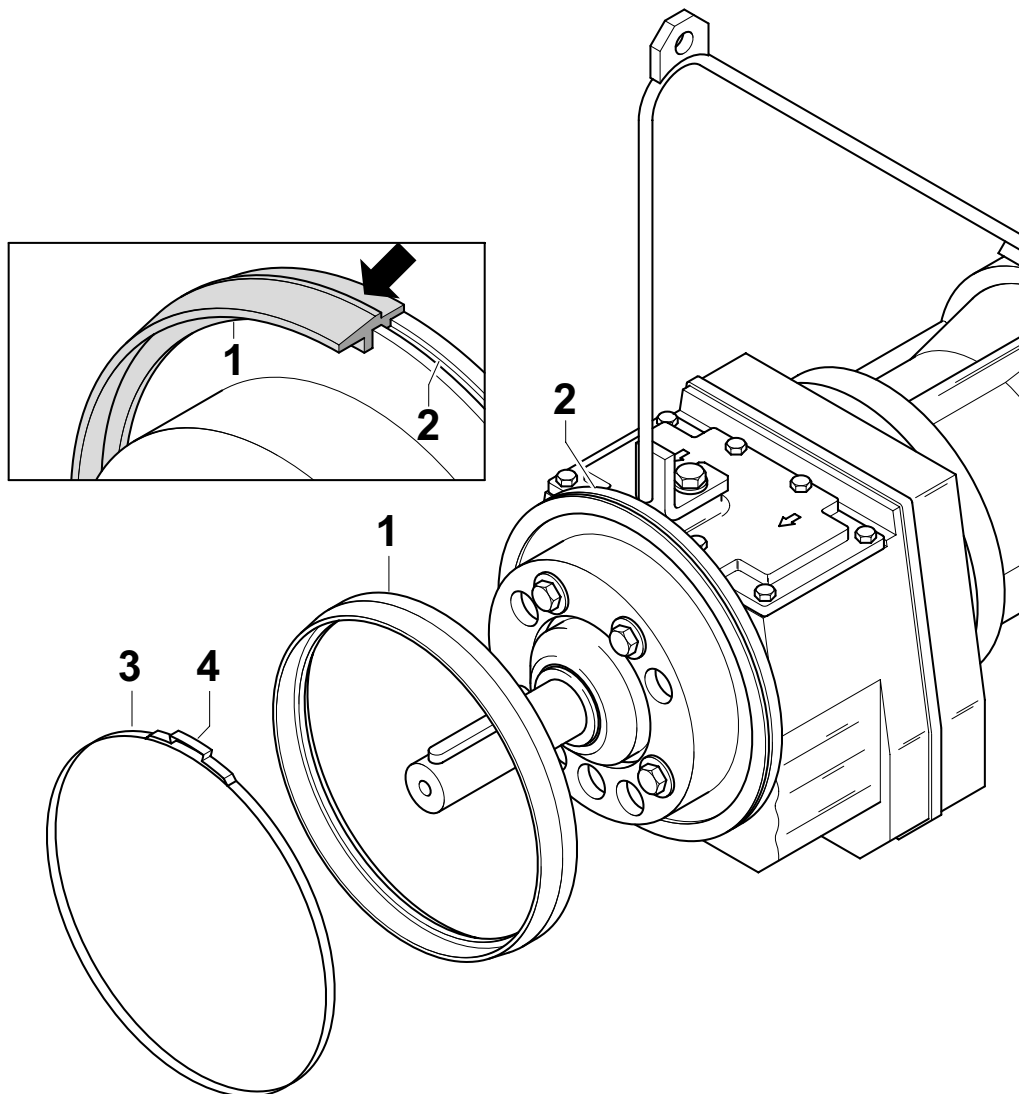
Montage/Demontage des Solids-Deflection-Ringes
